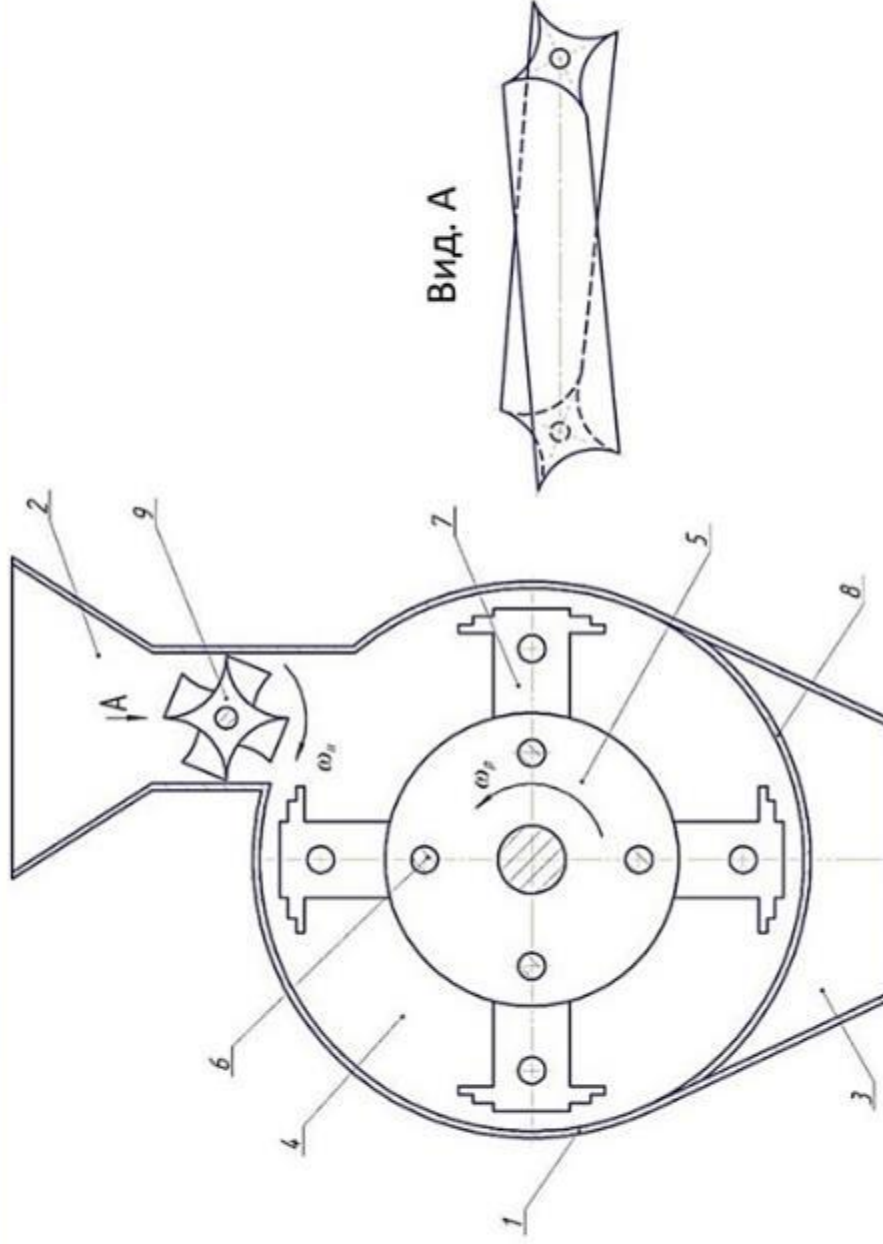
Молоткова дробарка: 1 - циліндричний корпус; 2 - завантажувальний бункер; 3 - вивантажне вікно; 4 - дробильна камера; 5 - ротор; 6 - палець; 7 - решето; 8 - решето; 9 - живильне пристрій
